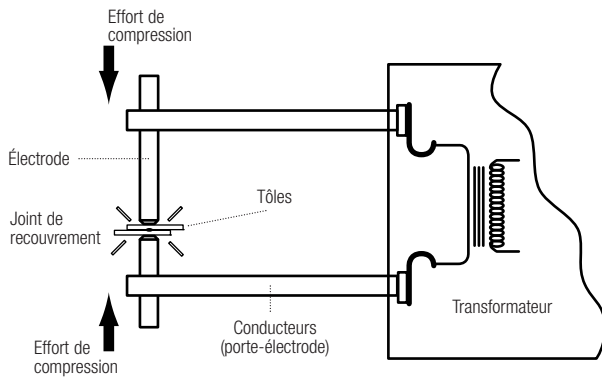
Soudage par résistance par point (RSW)
